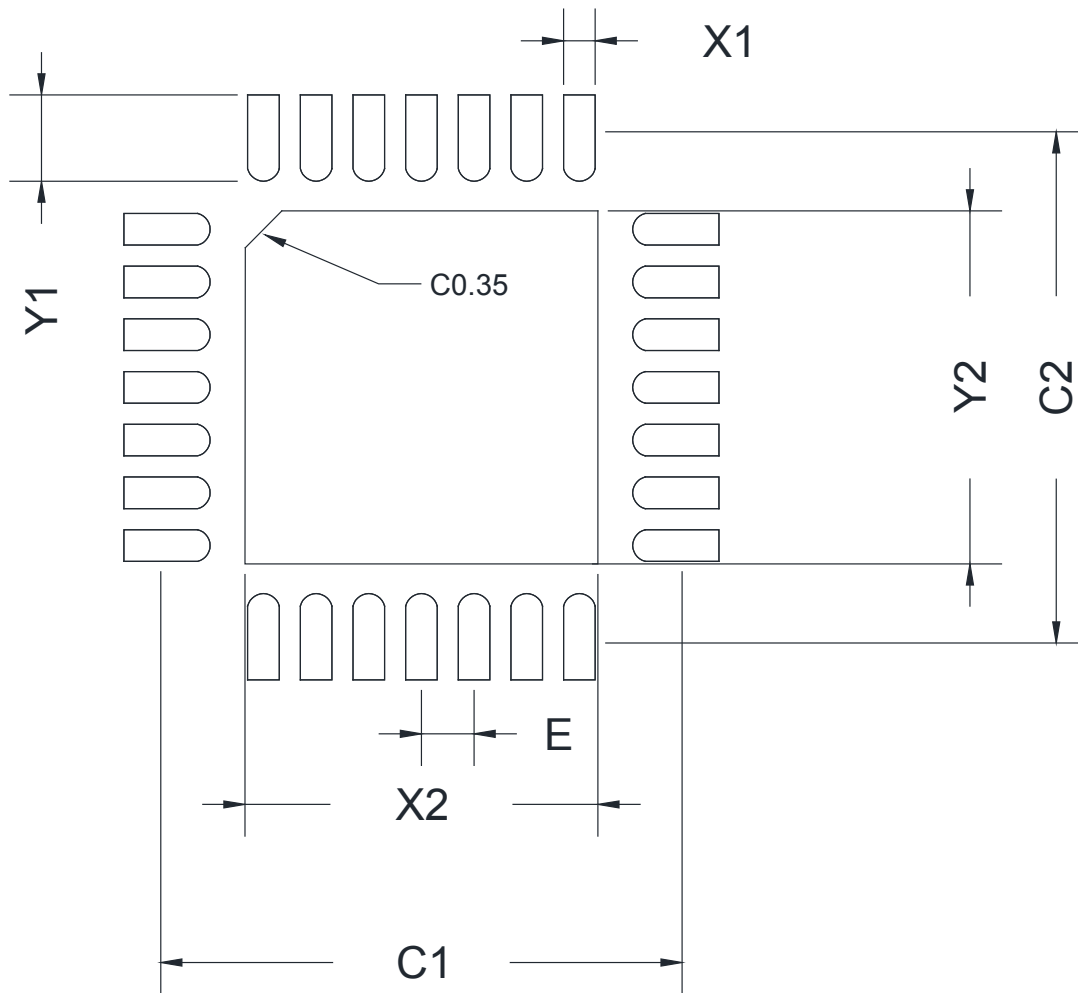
QFN28 PCB 焊盘布局图
